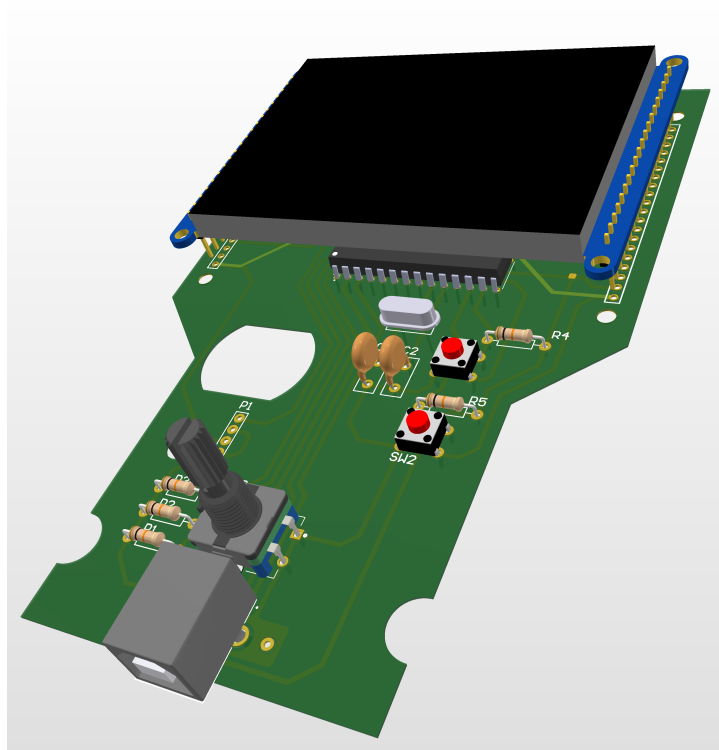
Vista isométrica frontal 3D del prototipo 1 de la PCB
